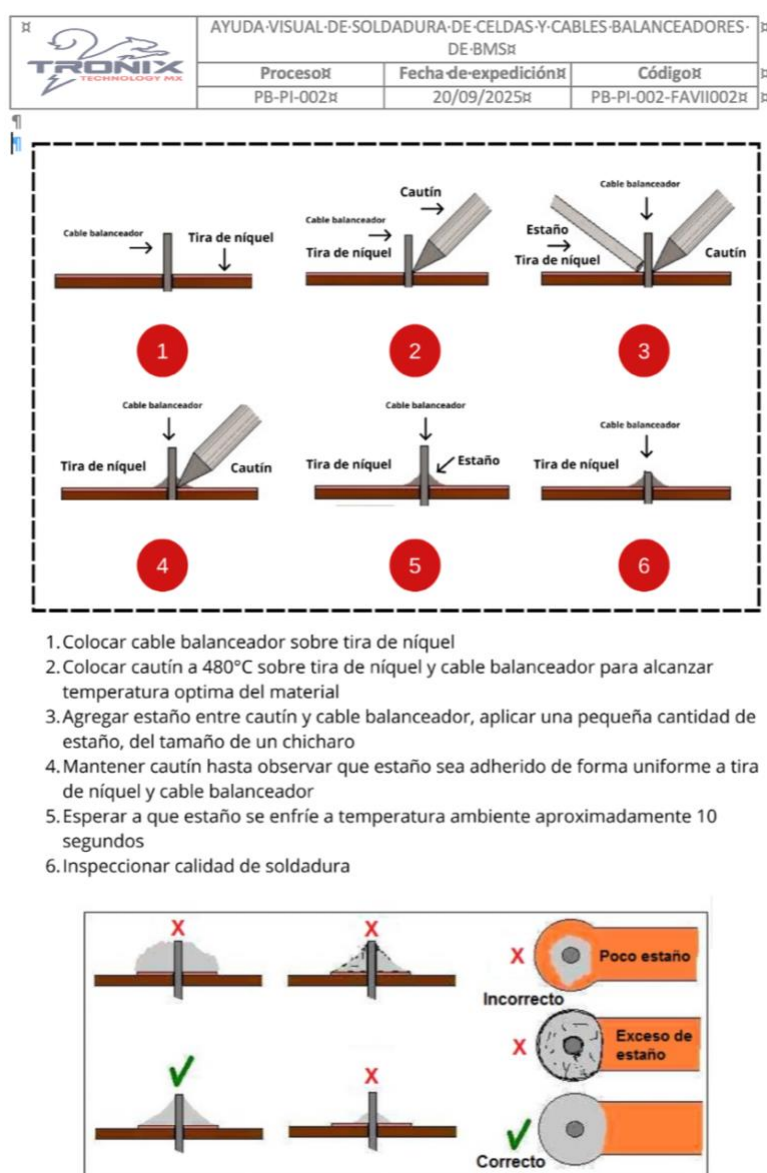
Ayuda visual de soldadura de celdas y cables balanceadores de BMS. Elaboración propia.
